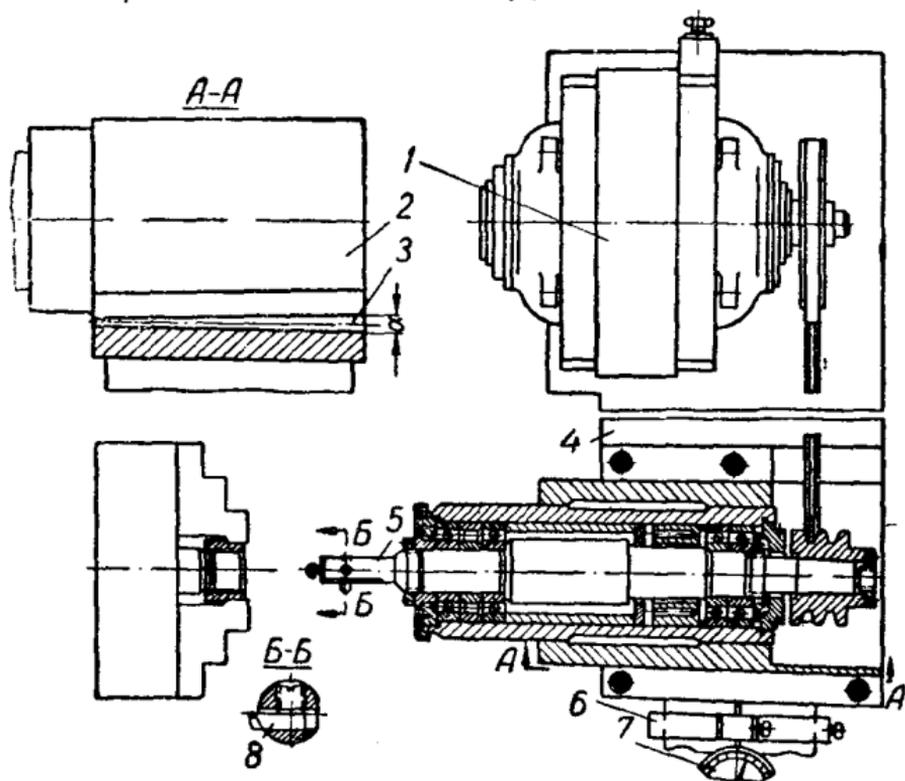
Приспособление для вихревого нарезания внутренней резьбы.
